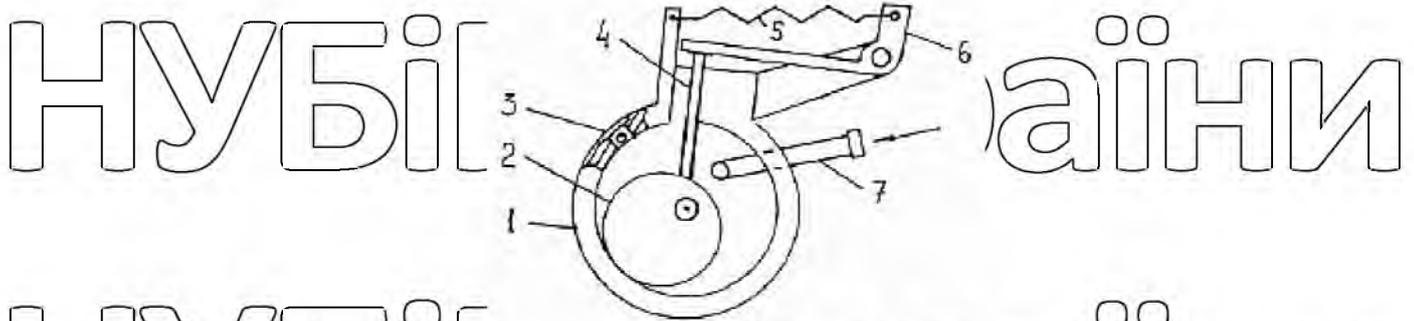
Схема вакуумного насоса з переколювальним ротором: 1 - корпус; 2 - ротор; 3 - вихлопний клапан; 4 - пластина; 5 - пружина; 6 - важіль; 7 - всмоктувальний патрубок.
